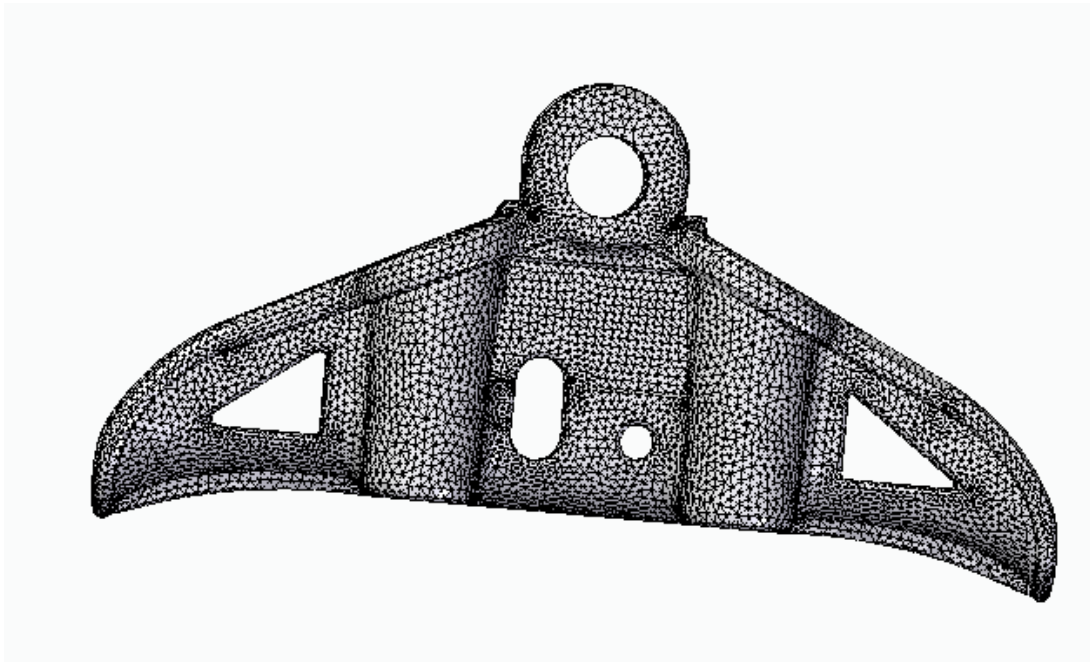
Mallado pieza final. Fuente: elaboración propia
